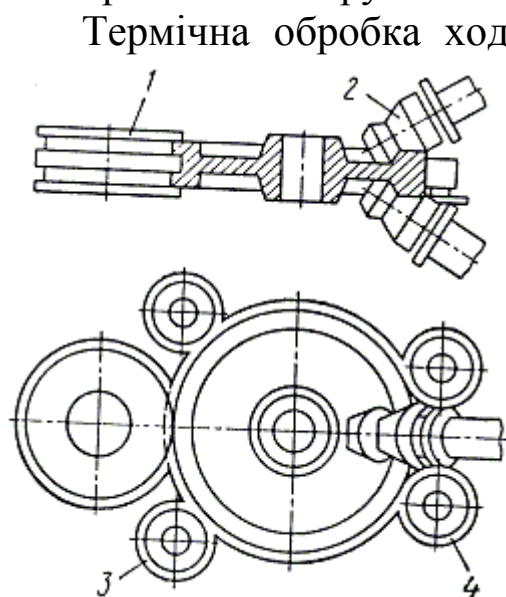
Схема розташування валиків в колесопркатному стані: 1 – корінний валик; 2 – похилий валик; 3 – направляючий ролик; 4 – натискаючий ролик.
